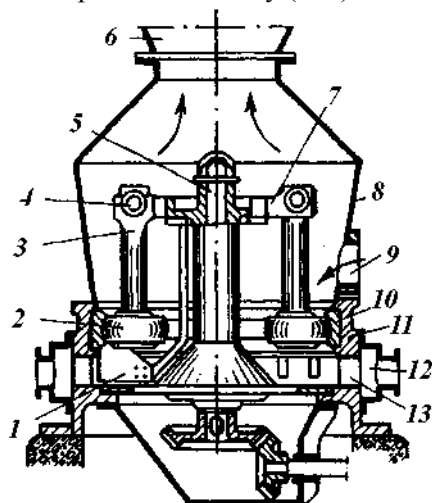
Конструкция маятниковой мельницы: 1 – скребки; 2 – ролики; 3 – штанги роликов; 4 – шарниры; 5 – центральный вал; 6 – сепаратор; 7 – крестовина-водило; 8 – кожух; 9 – штуцер питания; 10 – размольное кольцо; 11 – станина; 12 – воздушный короб; 13 – окна для воздуха.
